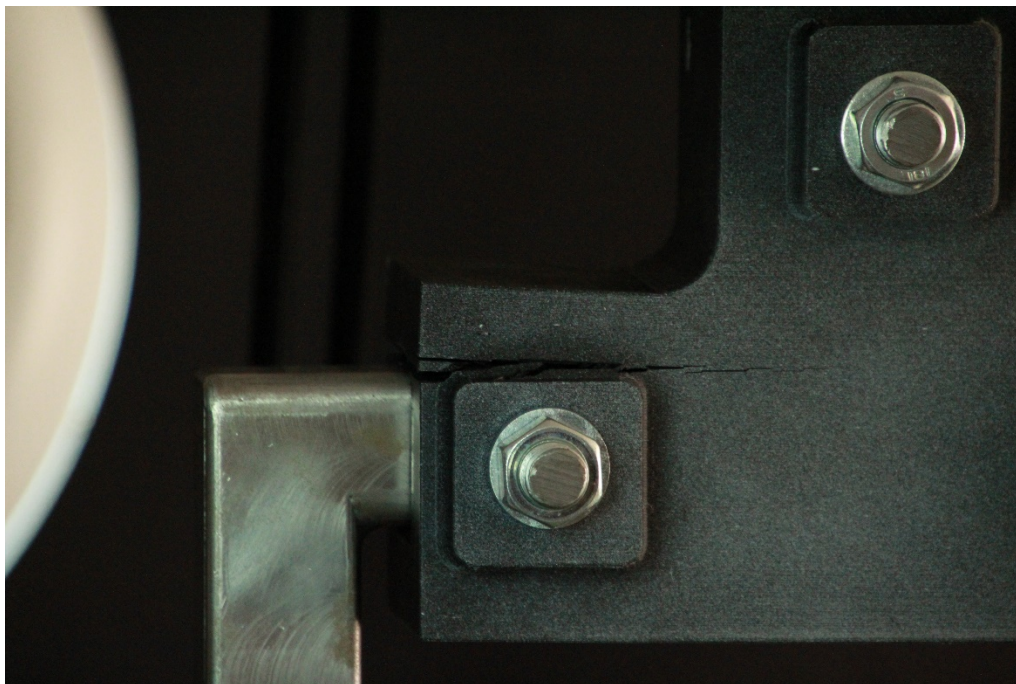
Detalle 2 de rotura del Prototipo 1 a compresión.
